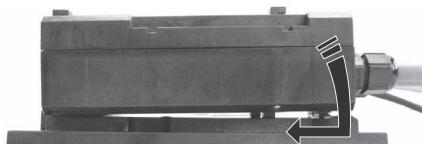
Montage de l'E-Box sur la plaque de fixation
